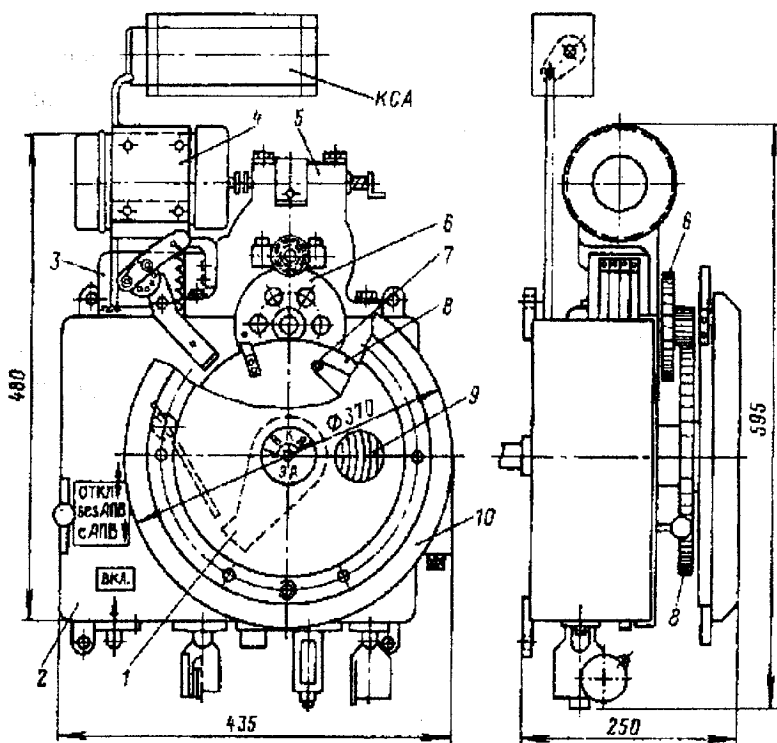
Пружинний привод з двигунним редуктором ППМ-10
